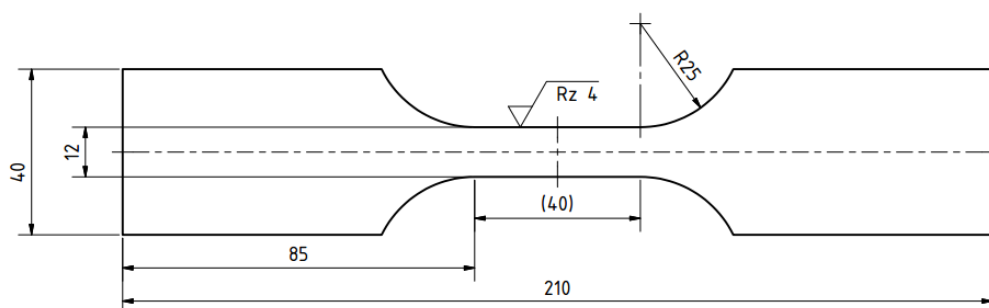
Эскиз образца для проведения испытаний сварных соединений на растяжение
